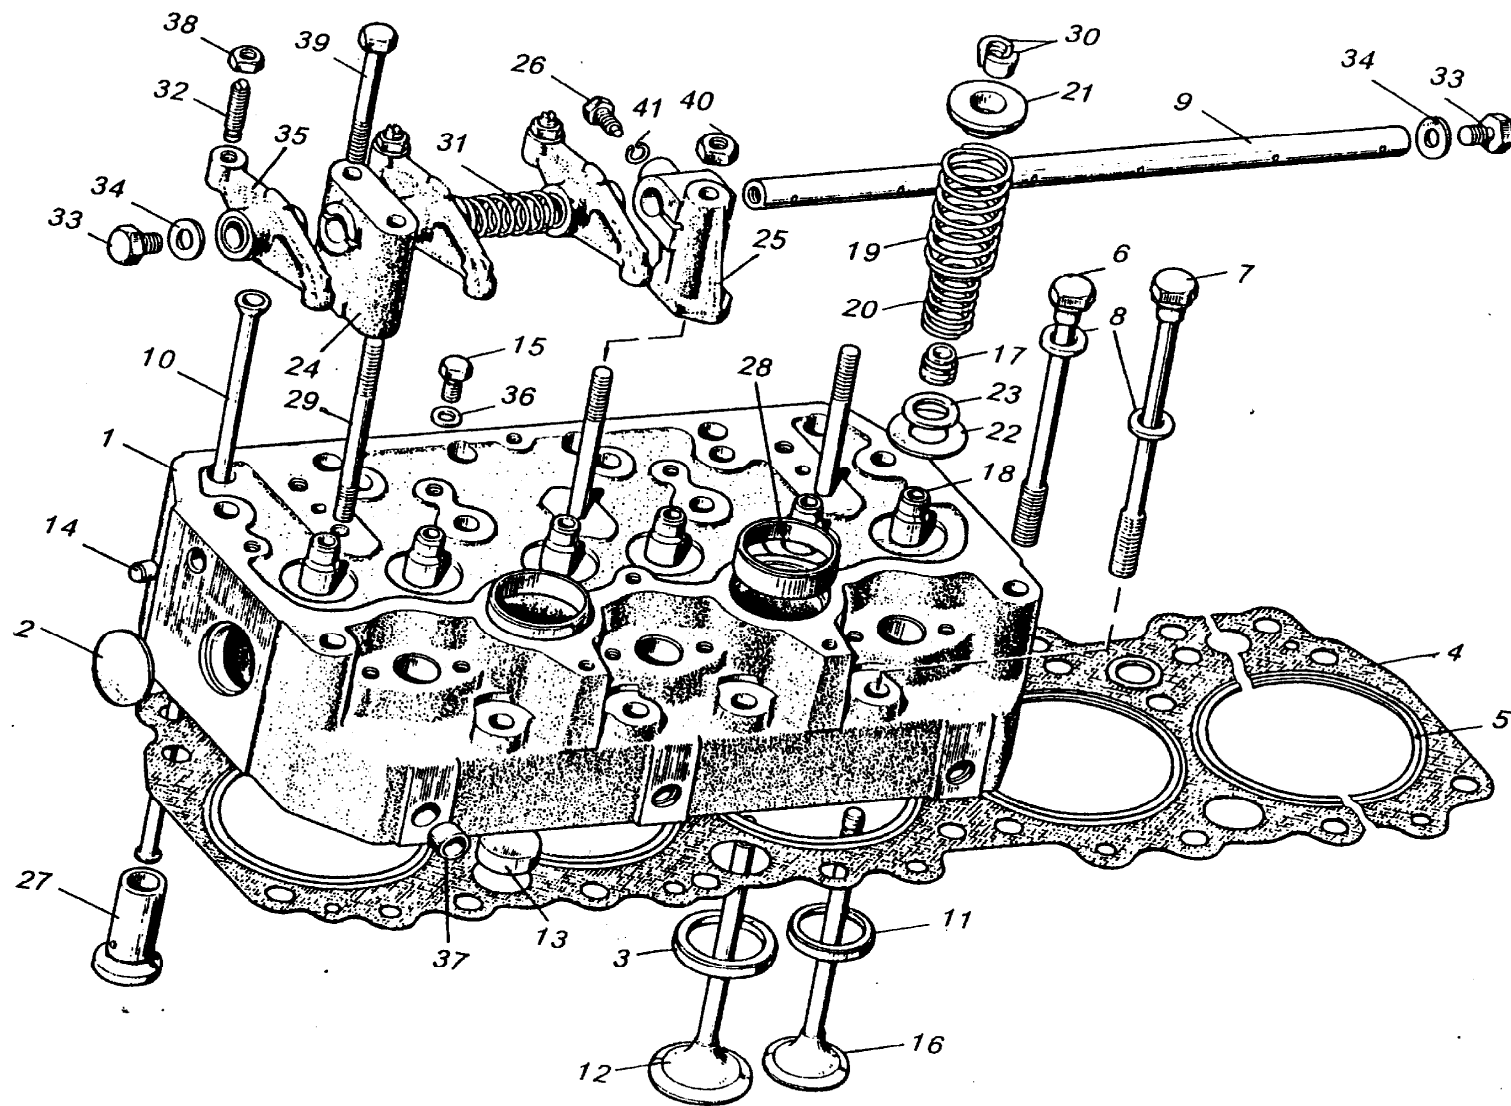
Головка цилиндров. Клапаны и толкатели клапанов
